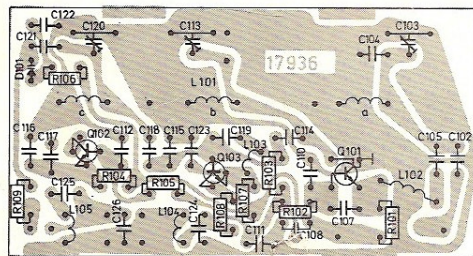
FM-tuner under serie nr. 1258300, sett fra foliesiden.
